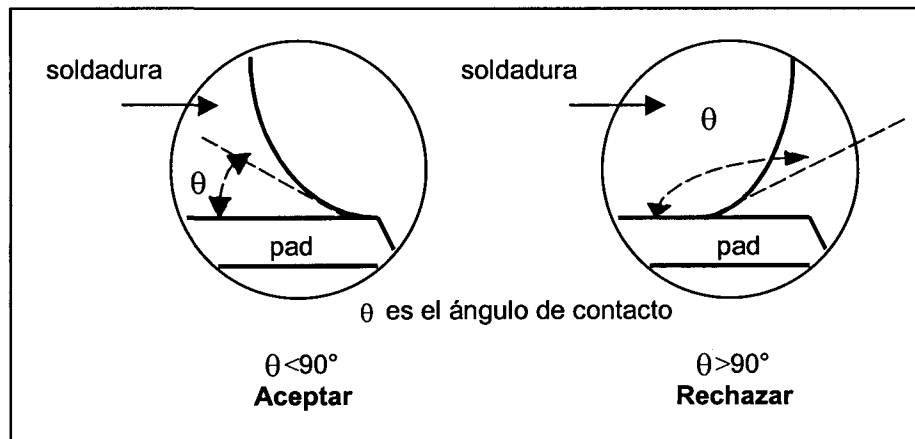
Ángulo de contacto en la soldadura.
